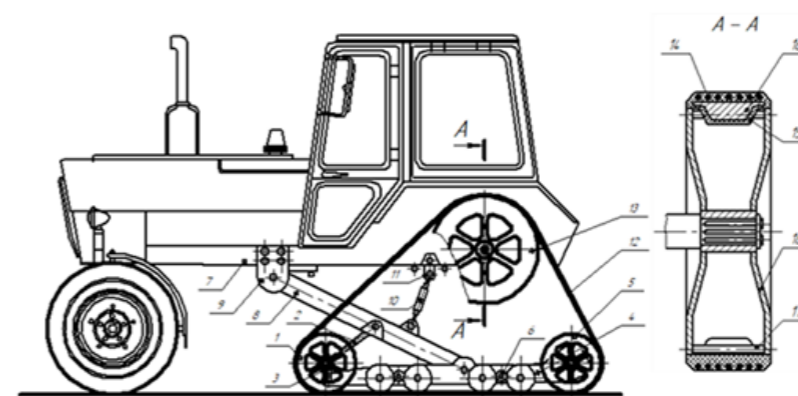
Полугусеничный движитель с резиноармированными гусеницами
